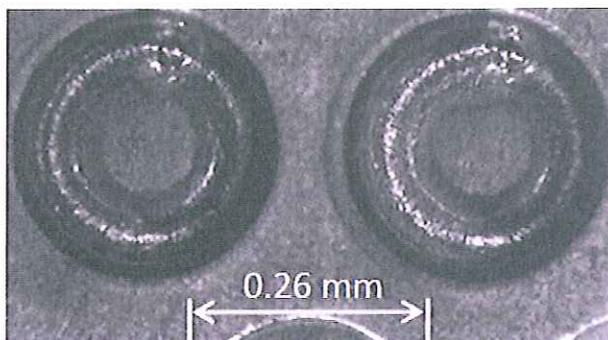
Soudage laser d'une plaque perforée (0,5 mm) sur un support
